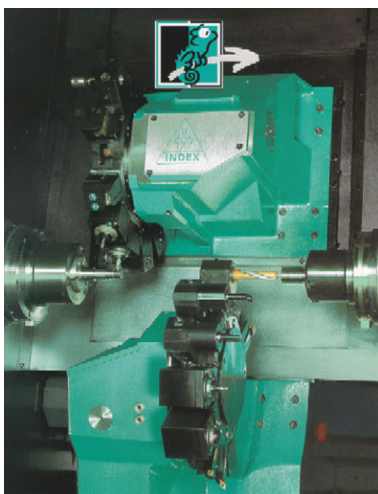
reZ) Mehrere Werkzeugträger (Boehringer)
